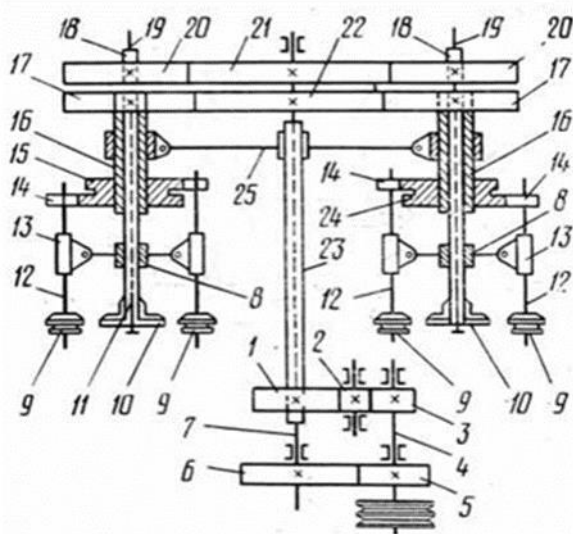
Багатопозиційний закручувальний механізм.
